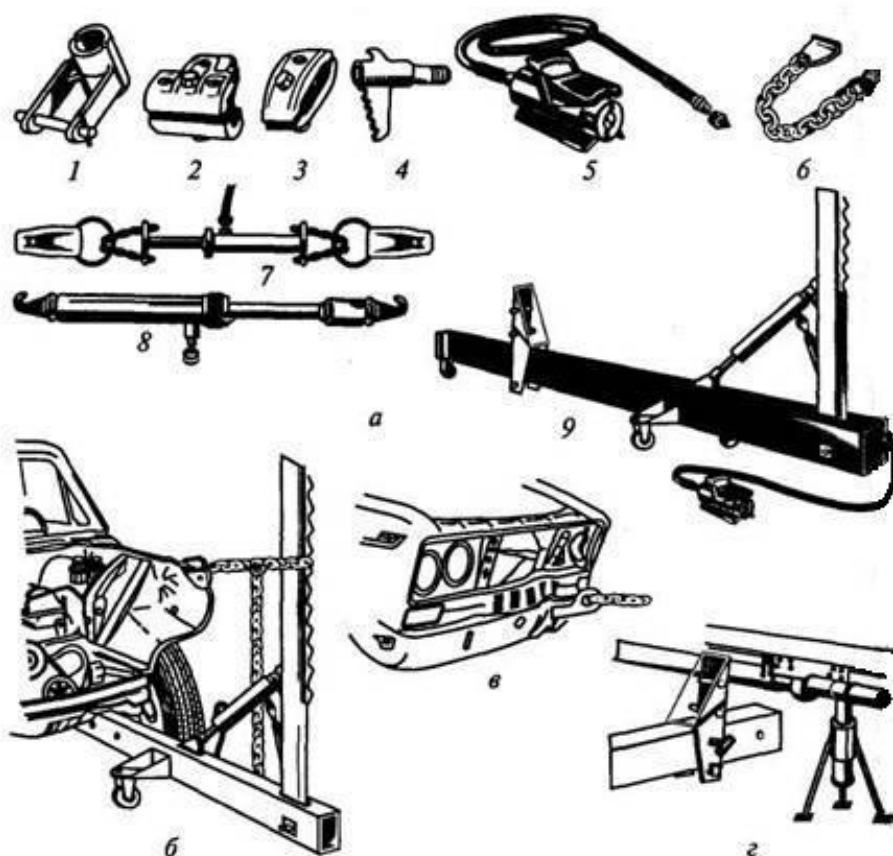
Приспособления для выполнения правки деформированного участка кузова:
